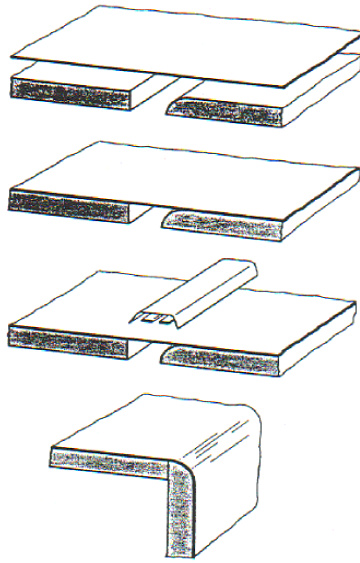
Kompaktplatte aus vorgefrästen Teilen
